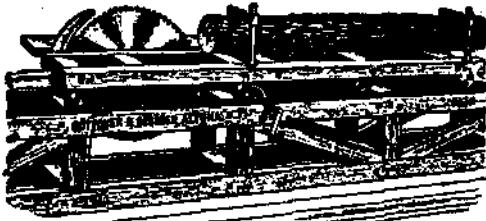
Станок с круглой пилой и подачей посредством коленчатой рукоятки.
